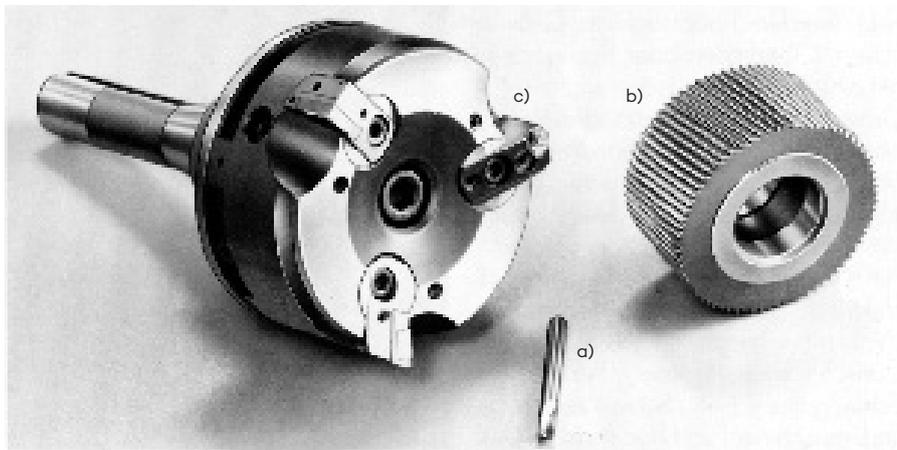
Fräsen von PLEXIGLAS® mit Walzenstirnfräser; weitere verschiedene Fräser-Typen: a) Zweischnieder, b) Walzenfräser, c) Diamantfräser
